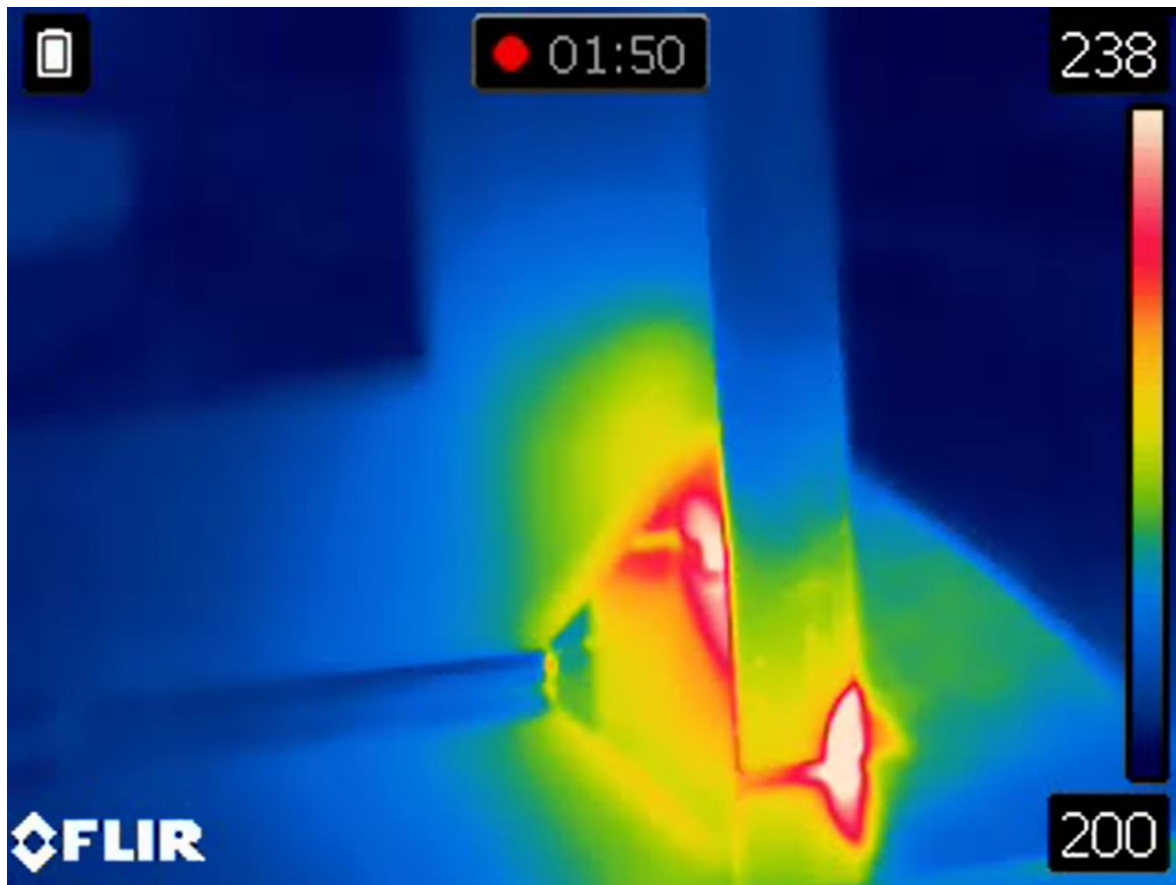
Piezas utilizadas para el proceso de soldadura
